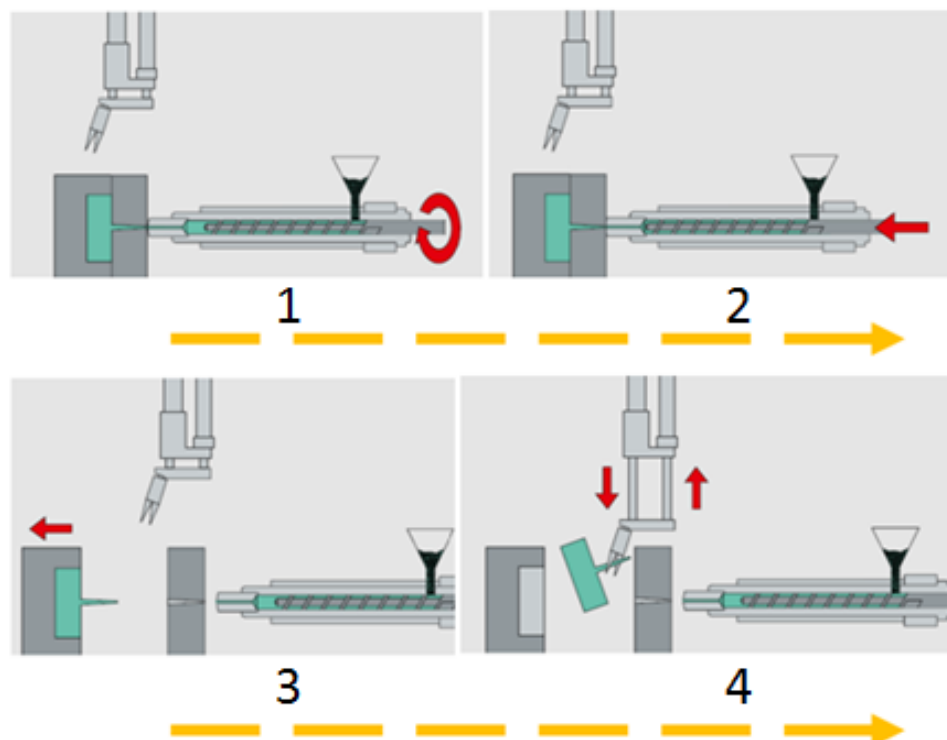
Sequência do processamento de um molde numa máquina injetora.
